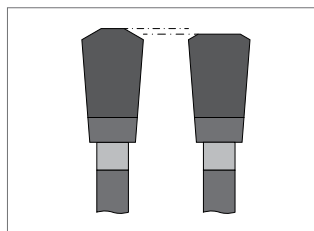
Dente trapezoidal - plano - biselado (TR-F-Fa)
